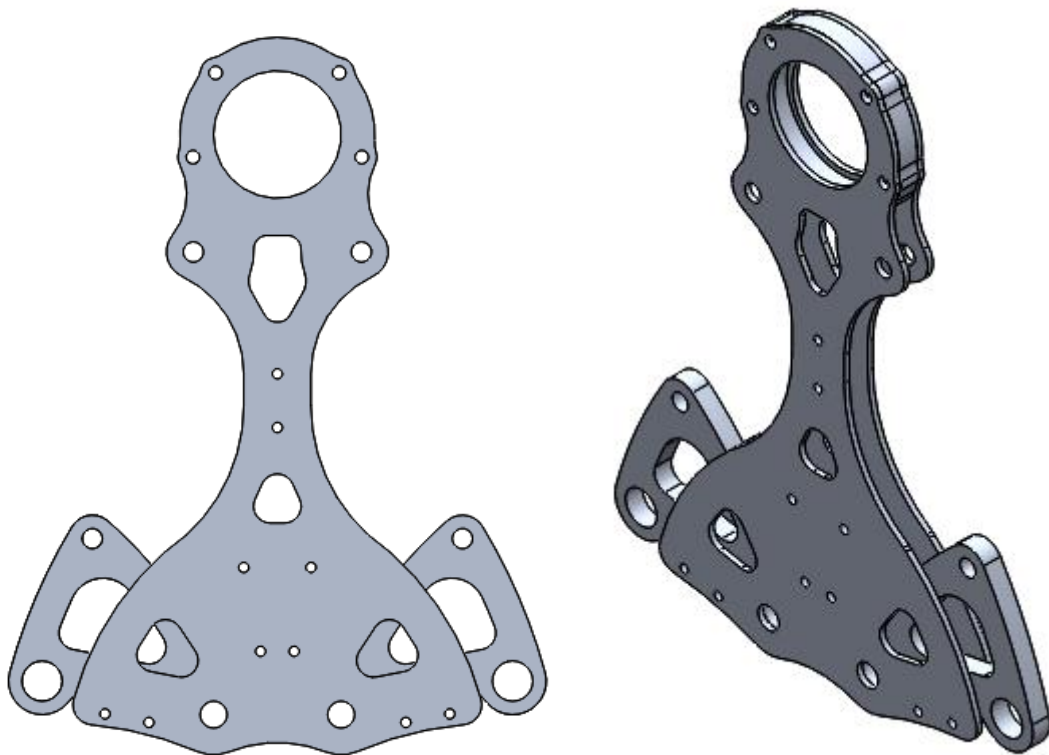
Vistas frontal e isométrica del conjunto cuerpo principal
